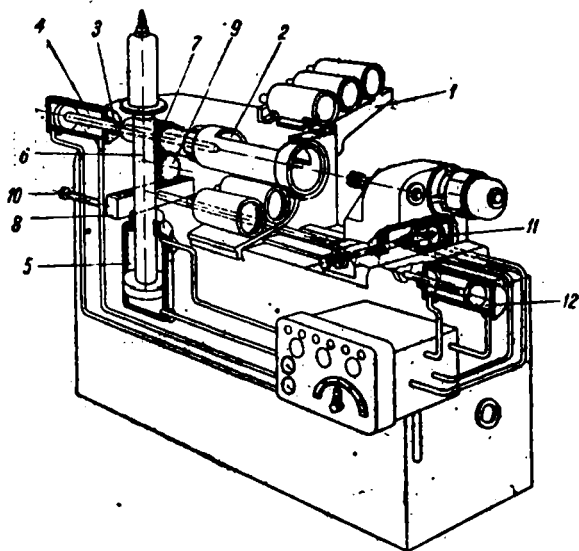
Механизм регулировки осевого положения шпинделя (резьбофрезерный станок Хансон-Уитней).
